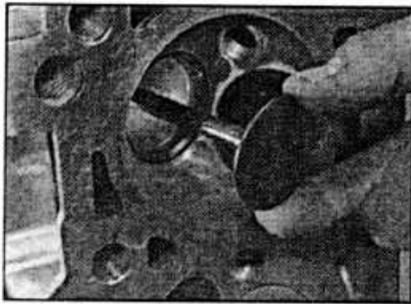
D.41. Установка клапана в головку блока цилиндров.
